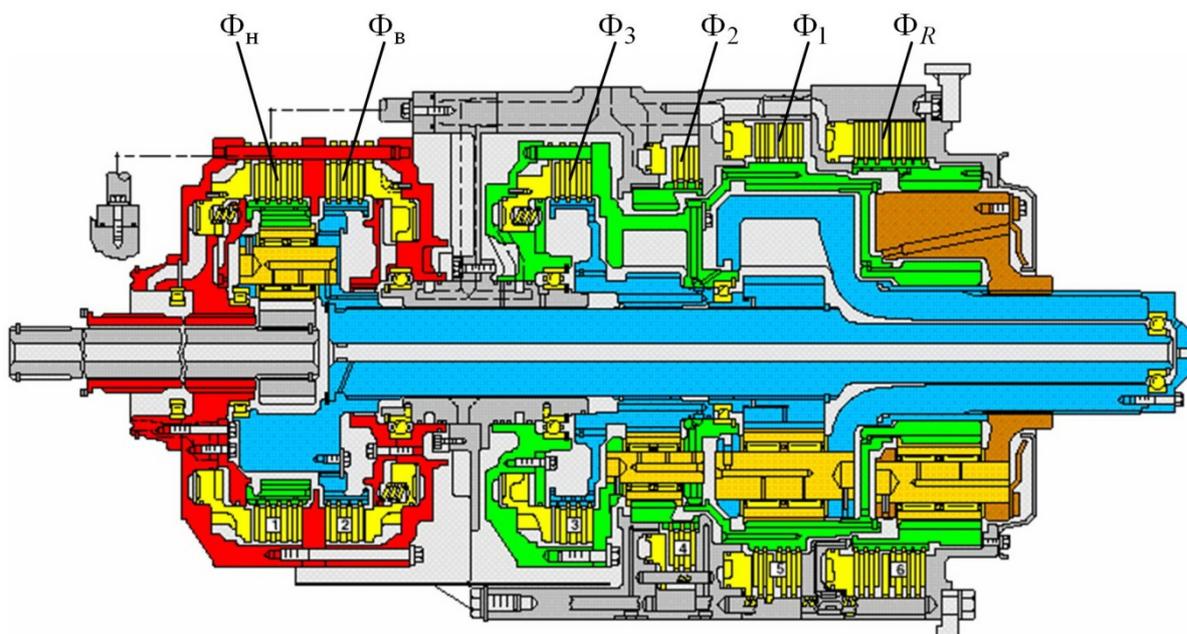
Конструкция планетарной коробки передач Caterpillar
